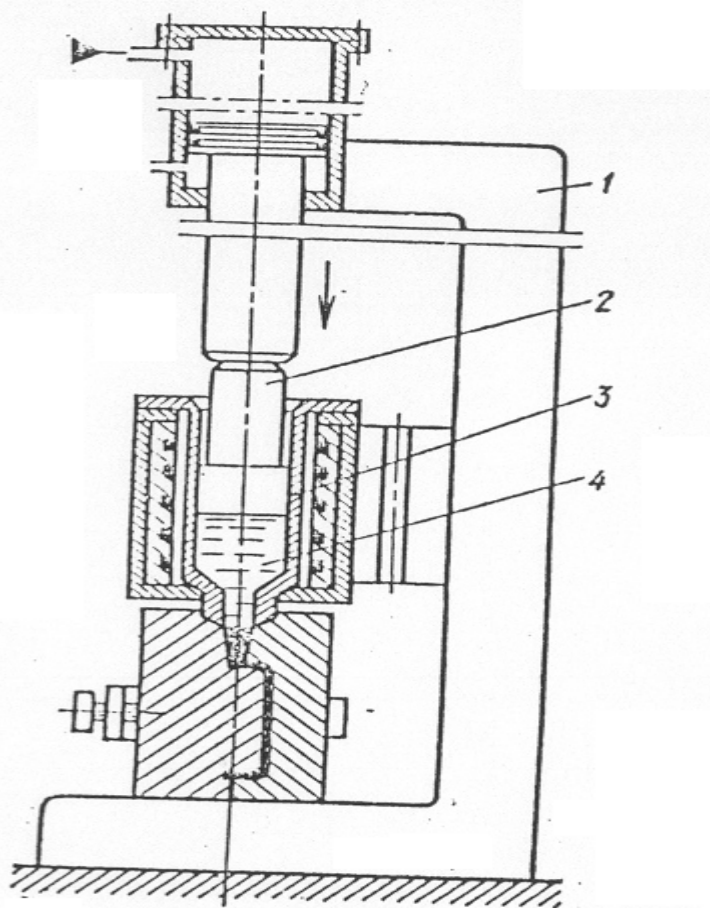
Схема устройства для запрессовки жидкого модельного состава: 1 – пресс; 2 – поршень; 3 – запрессовочное устройство; 4 – жидкий модельный состав.
